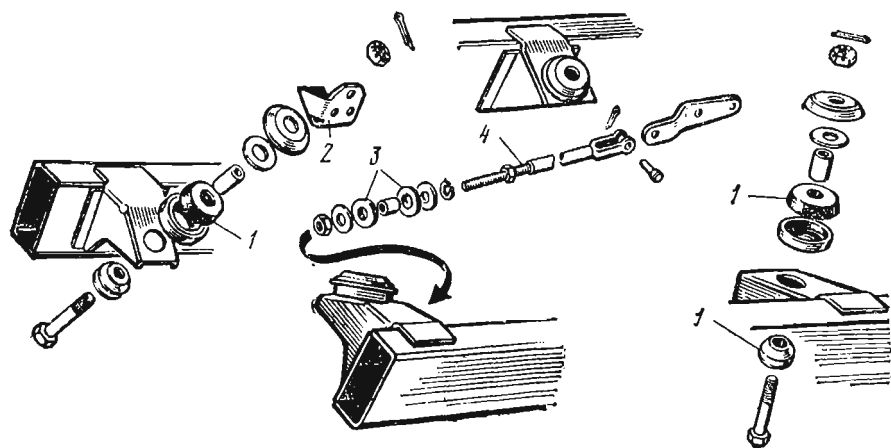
Крепление двигателя автомобиля УАЗ-469
